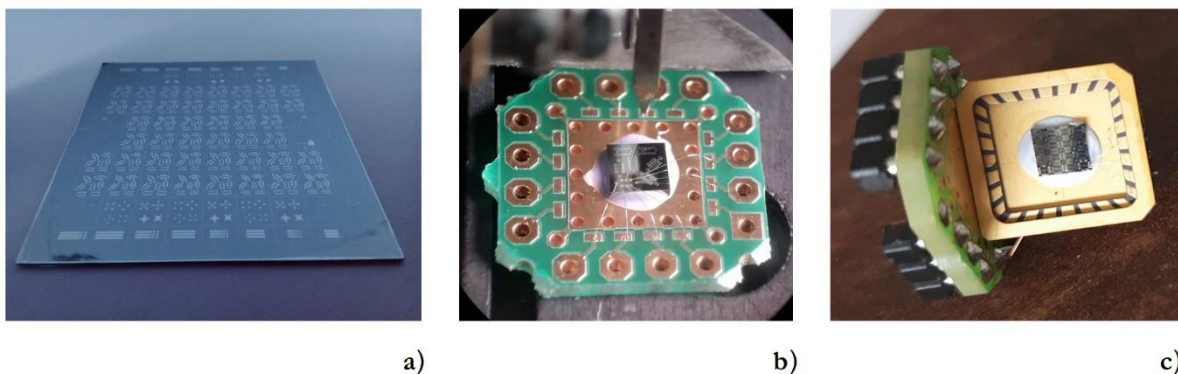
Übersicht der AVT. a) zeigt ein prozessiertes Bruchstück mit Hall-Elementen vor der AVT. b) zeigt eine final aufgebaute Hall-Struktur und c) ein Spin-Ventil Bauelement nach der AVT.
